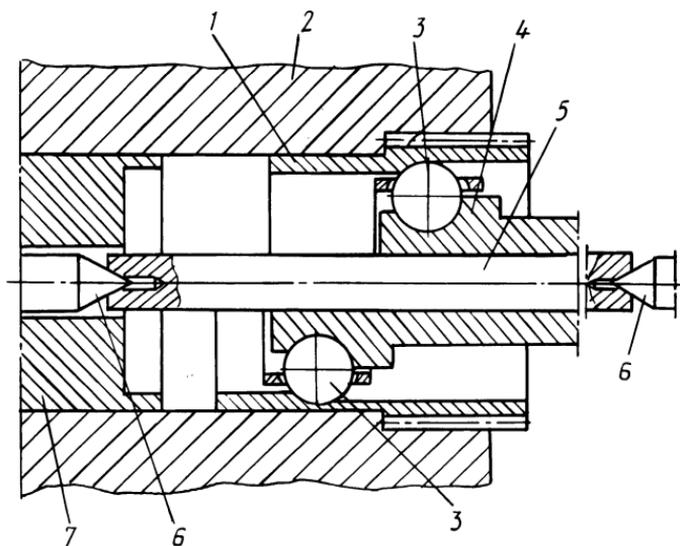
Получение гибкого зубчатого звена ротационной вытяжкой, сочетающей деформирование заготовки по прямой и обратной схемам
